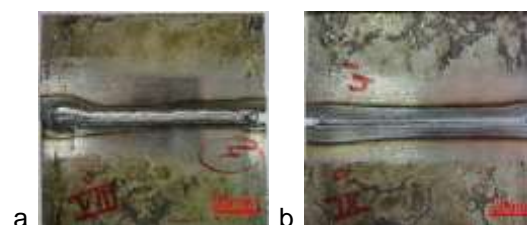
Cordones de soldadura a) GMAW; b) PAW.
